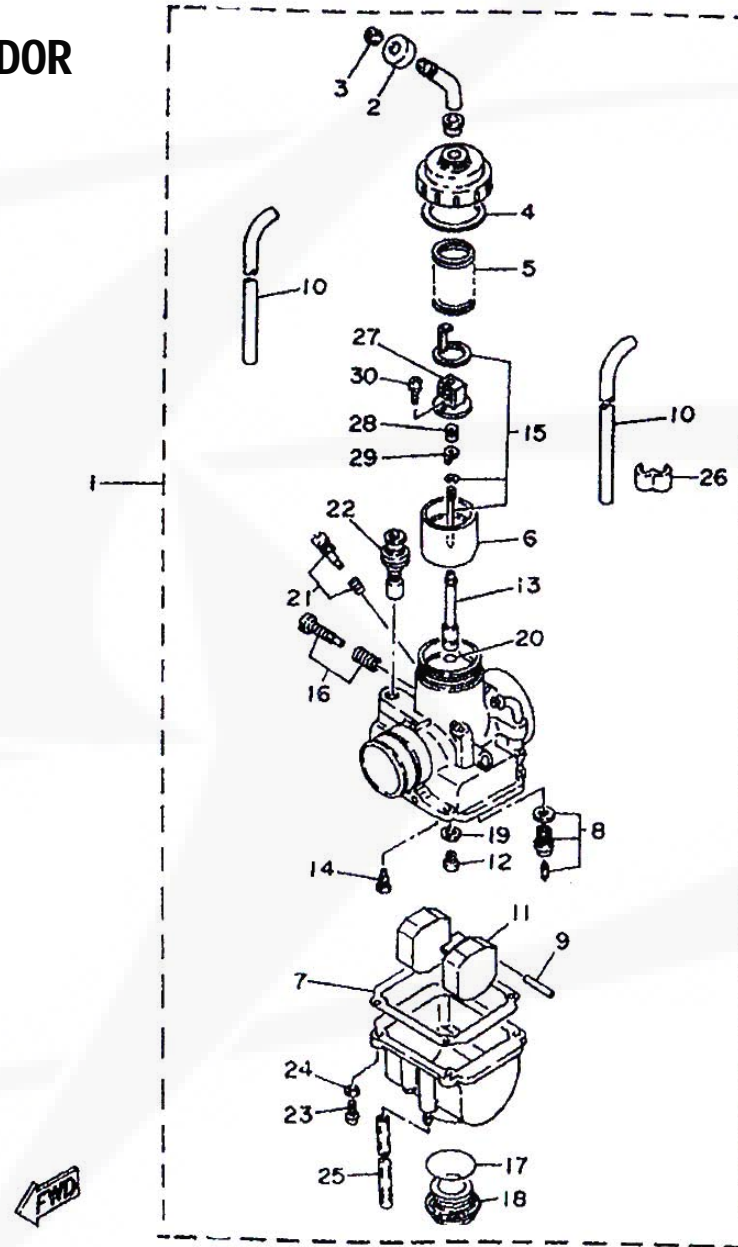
CARBURATEUR / CARBURETOR / CARBURADOR
